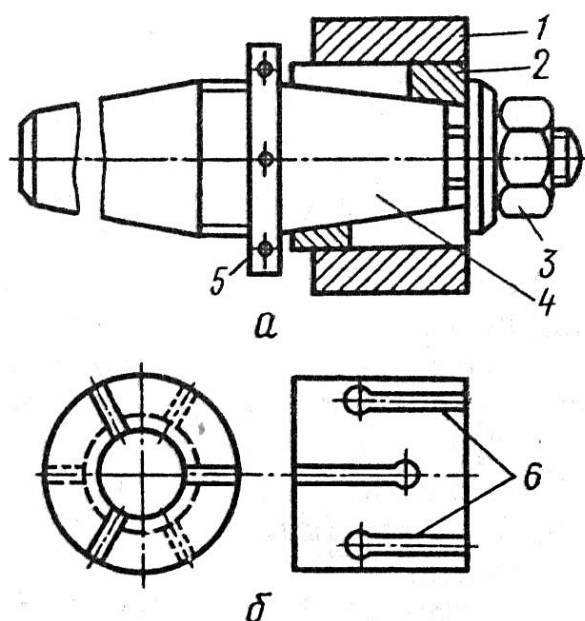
Разжимная оправка (а) и гильза разрезная (б)
